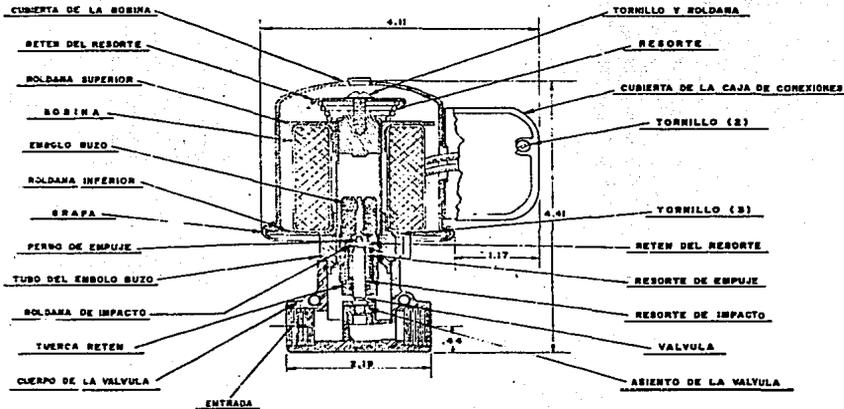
COMPONENTES DE UNA VALVULA SOLENOIDE
